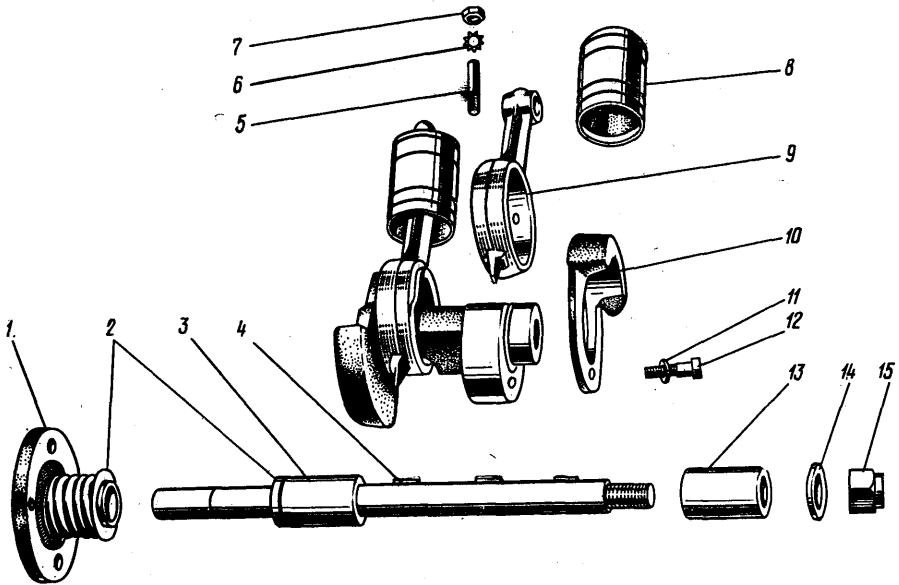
Детали механизма движения компрессора с эксцентриковым диском: 1 — крышка сальника; 2 — сальник вала в сборе; 3 — вал; 4 — шпонка; 5 — стопорный штифт; 6, 11 — замковая шайба; 7 — гайка стопорного штифта; 8 — поршень; 9 — шатун; 10 — противовес; 12 — винт; 13 — подшипник вала; 14 — шайба; 15 — стопорная гайка.
